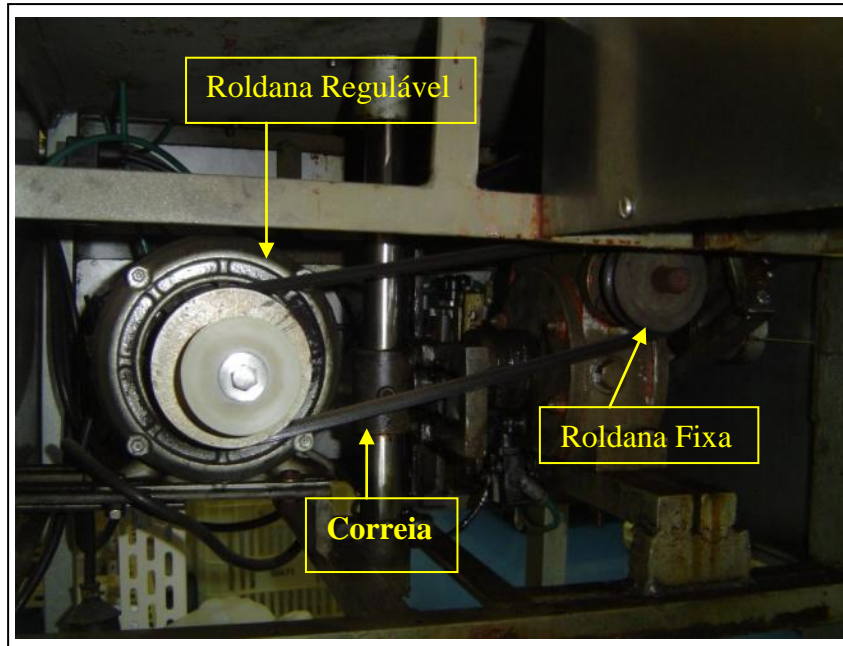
Roldanas da máquina tampadora de frascos.
